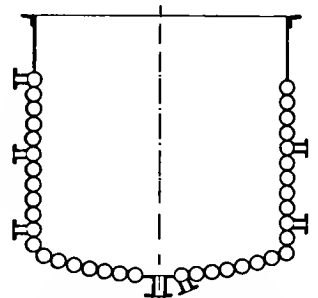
Schema eines Apparates aus geschweißten Schlangen.
